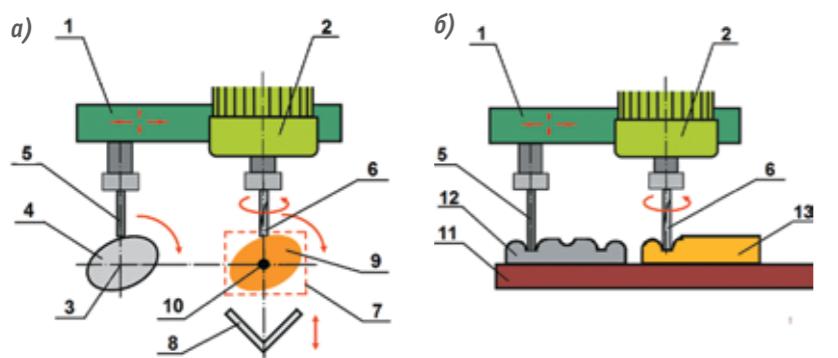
Схема объемно-копировального станка с концевыми фрезами
